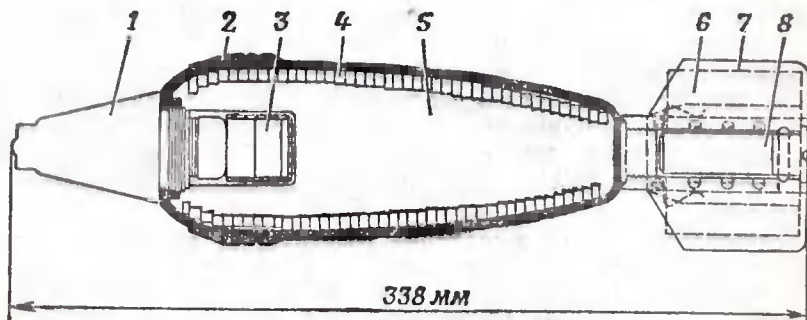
81-мм осколочно-фугасная мина с полуготовыми осколками, разработанная бельгийской фирмой РКВ: 1 — взрыватель; 2 — корпус; 3 — дополнительный детонатор; 4 — металлическая спираль с насечками для образования осколков; 5 — разрывной заряд; 6 — дополнительный лучок боевого заряда; 7 — стабилизатор; 8 — воспламенитель
